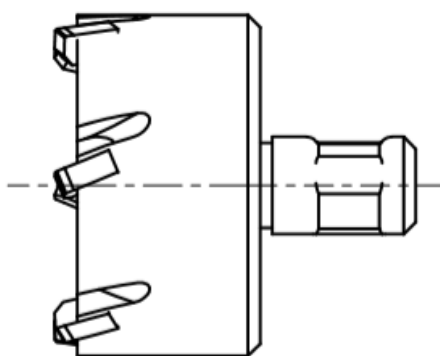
Свердло корончасте з твердосплавними пластинами
